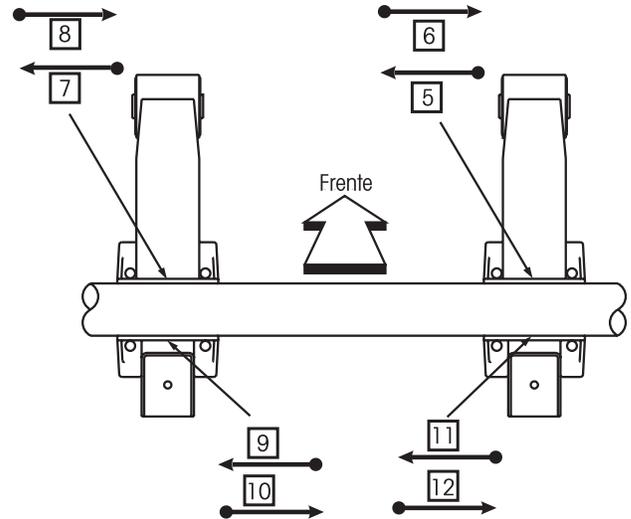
Secuencia de segundo y tercero cordones de soldadura
